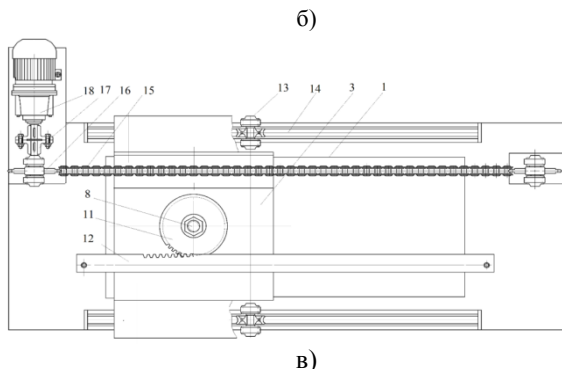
Предлагаемая конструкция устройства для производства арболита:
